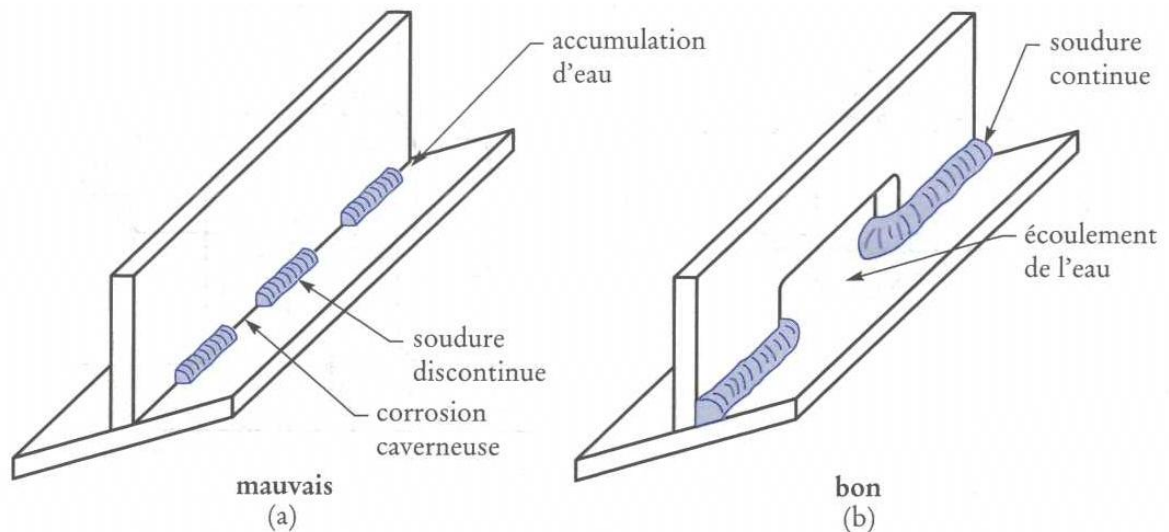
a) Un cordon de soudure discontinu engendre des interstices, sources de corrosion caverneuse. b) L'accumulation d'eau étant également une source de corrosion, il faut prévoir un bon écoulement.
